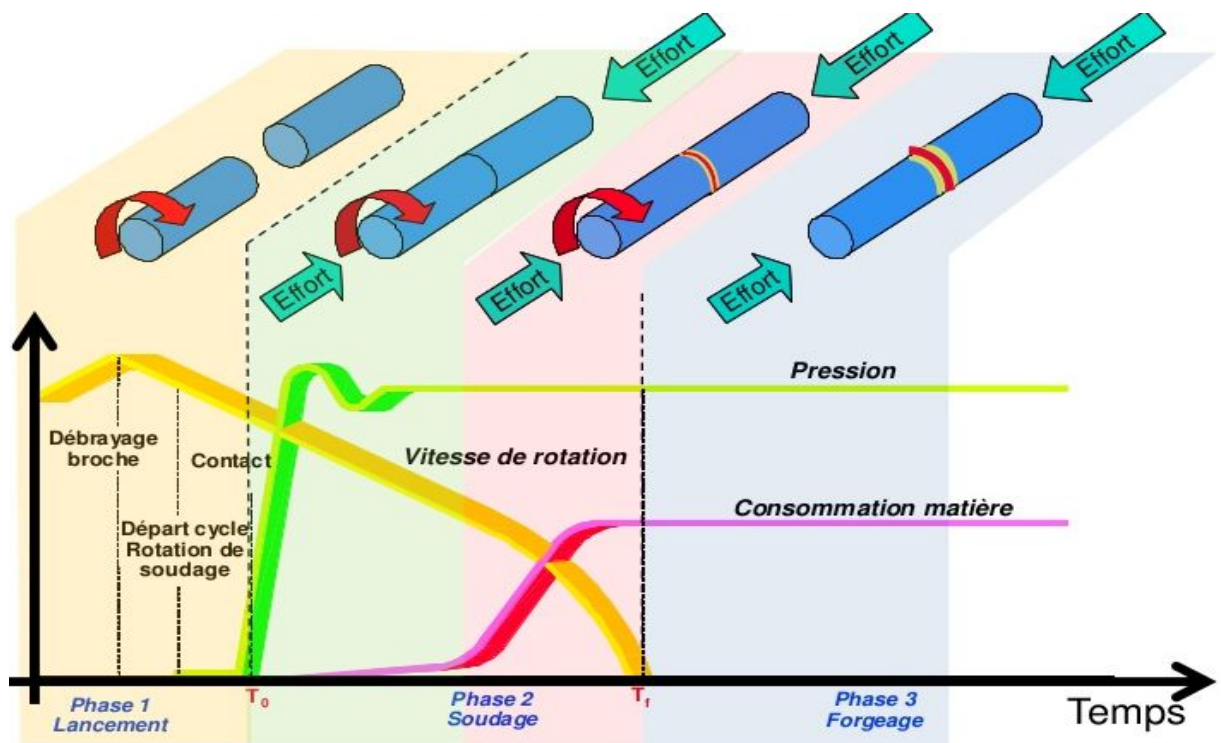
Le cycle de soudage par friction [18].
